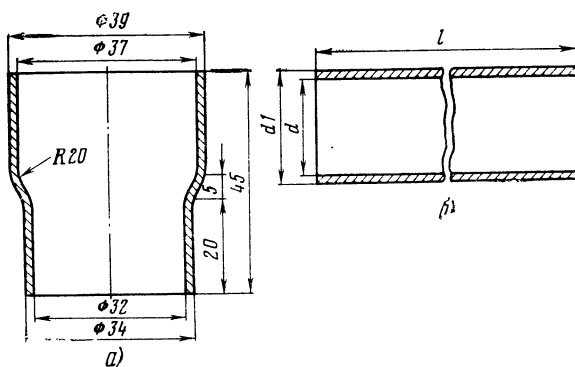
Алюминиевые детали для монтажа кабеля методом сварки взрывом:
